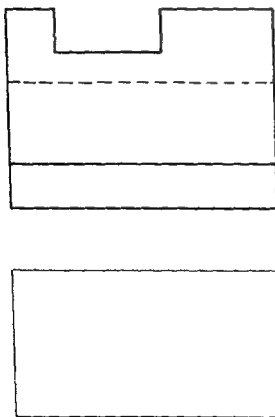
Dibujar la planta del objeto representado con alzado y perfil.
